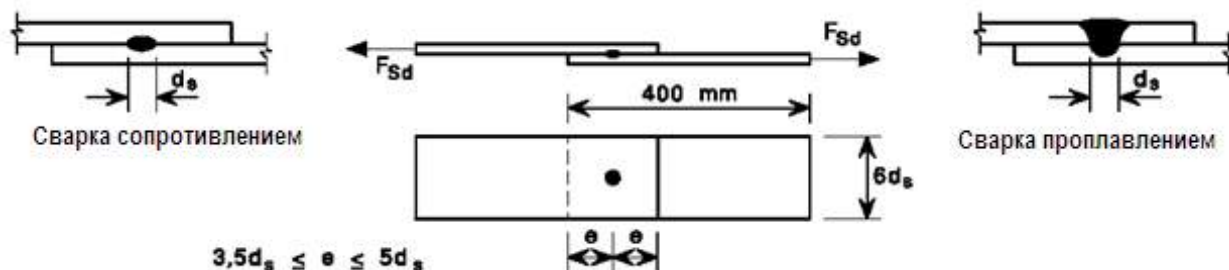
Образцы для испытаний на срез сварных точек
